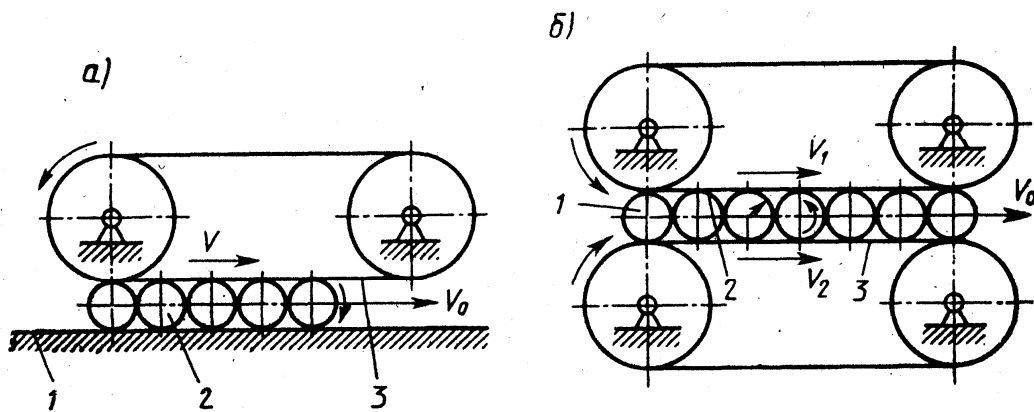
Конструктивна схема однострічкового транспортера
